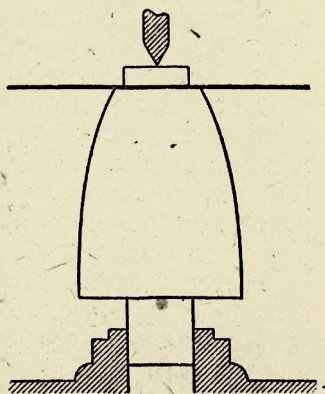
Патрон и платиновая пластинка, приготовленные для «давки» тигля.
